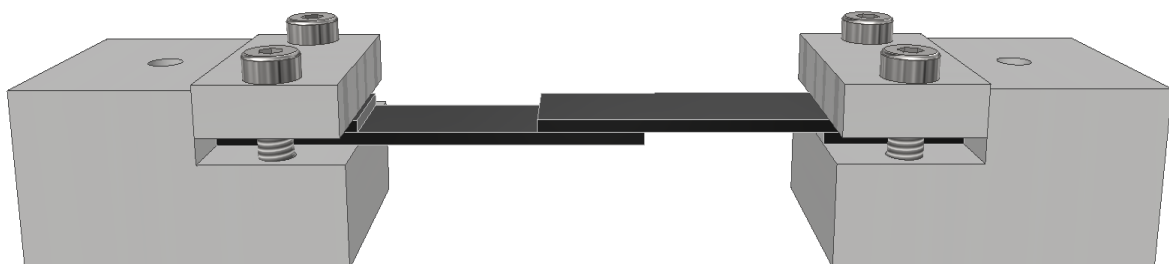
Esquema del montaje de la probeta SLJ en las garras de la máquina de ensayo. Fuente: elaboración propia.
